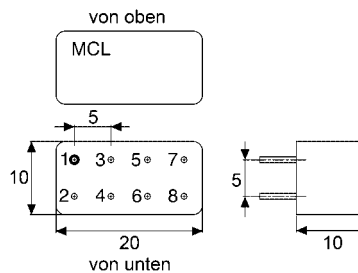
Gehäuse der PDC-xxx; ein blauer Ring auf der Unterseite markiert das Pin 1.
